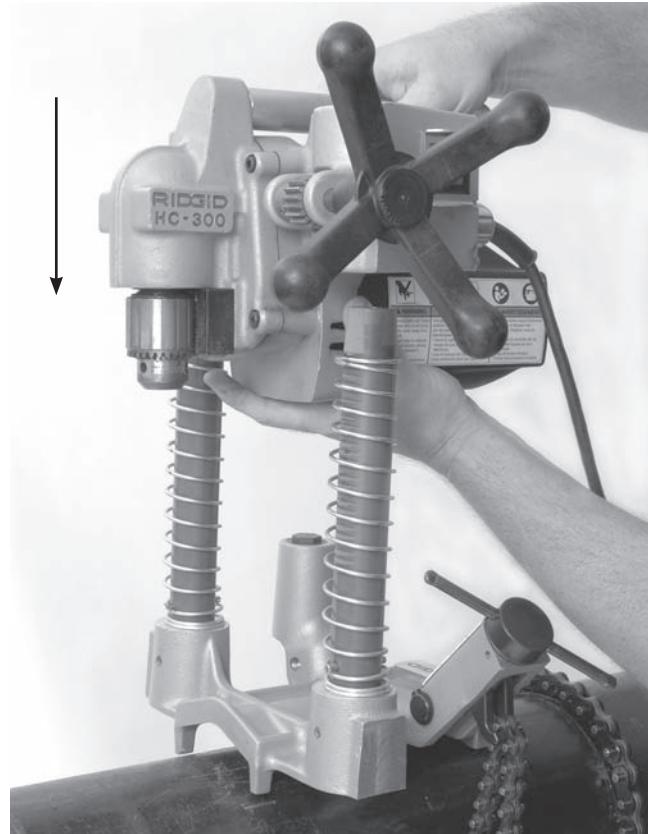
Oddeľenie zostavy základne a zostavy motora
